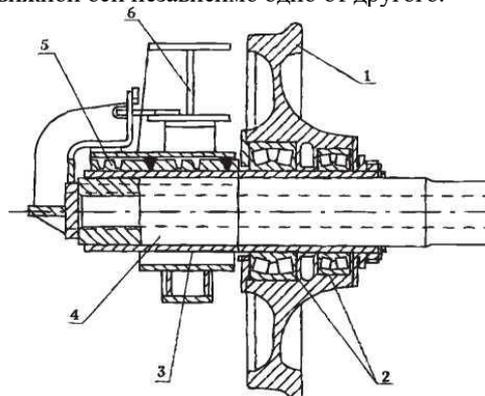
Колёсная пара конструкции Н. Гайдарова
